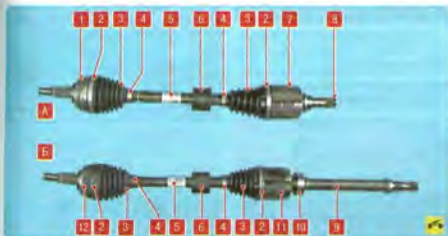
Приводы передних колес автомобиля ZWD: А – привод левого переднего колеса; Б – привод правого переднего колеса; 1 – наружный шарнир привода левого переднего колеса; 2 – большие хомуты крепления чехлов шарниров; 3 – чехлы шарниров; 4 – малые хомуты крепления чехлов шарниров; 5 – валы приводов передних колес; 6 – динамические демпферы; 7 – внутренний шарнир привода левого переднего колеса; 8 – стопорное кольцо внутреннего шарнира привода левого переднего колеса; 9 – промежуточный вал привода правого переднего колеса; 10 – подшипник опоры промежуточного вала; 11 – внутренний шарнир привода правого переднего колеса; 12 – наружный шарнир привода правого переднего колеса
